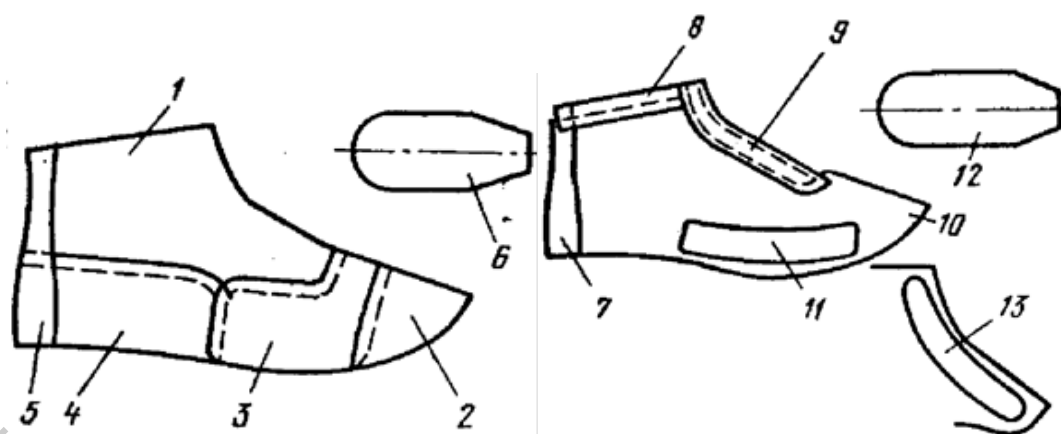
Детали верха ботинок с настрочными союзками:
